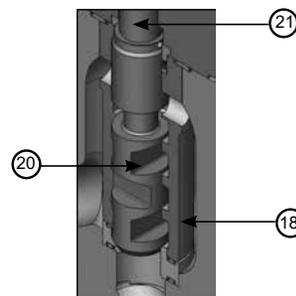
Направляющая поверхность заглушки, втулки и штока
